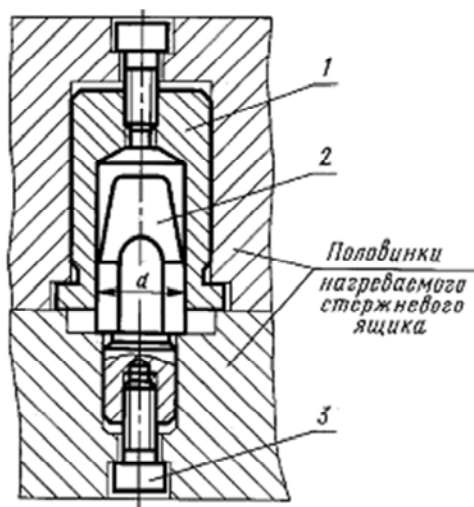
Конструкция центрирующего соединения с винтовым креплением
